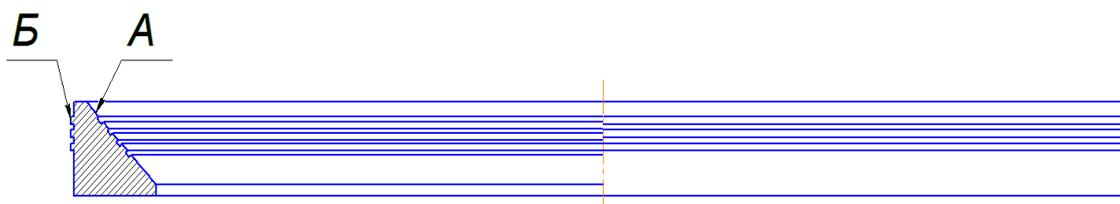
Поверхности для наплавки уплотнительного кольца
